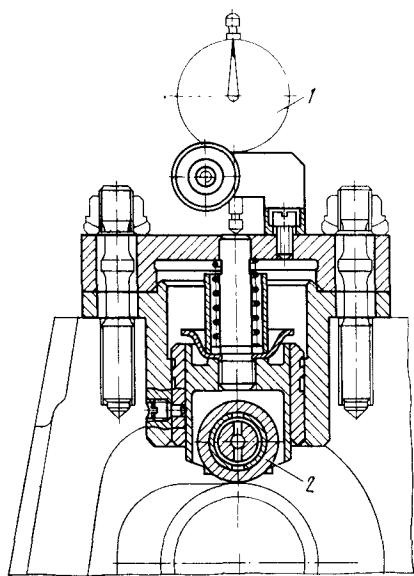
Приспособление для замера общего угла опережения подачи топлива
